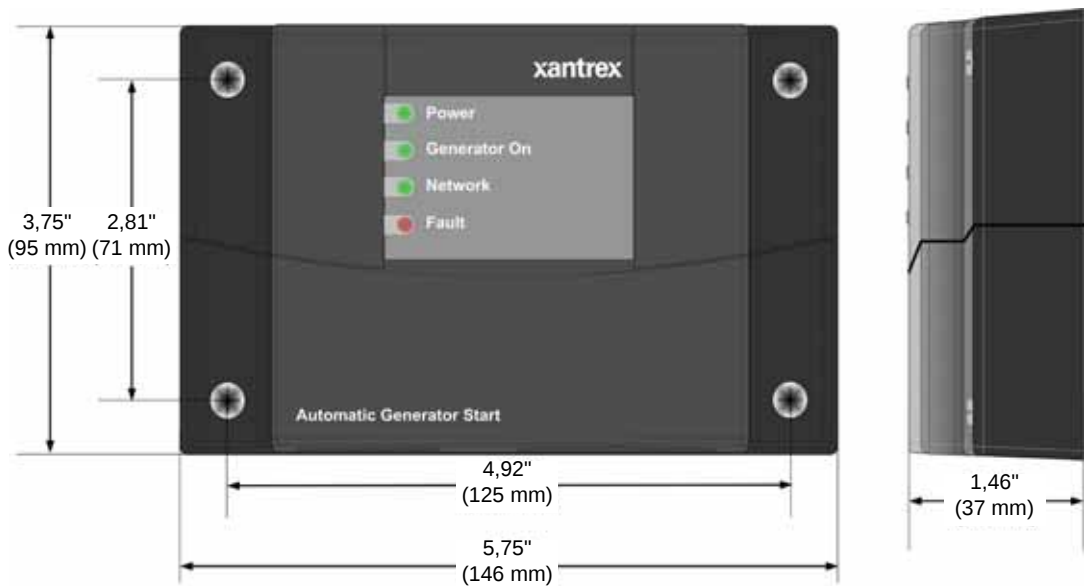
Dimensiones del módulo de arranque de generador automático XW
